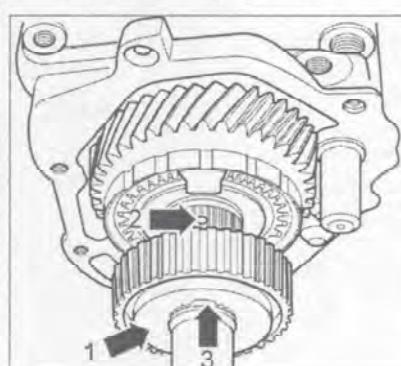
Напрессуйте ступицу синхронизатора 5-й/6-й передач без зазора. Буртик ступицы (стрелка 1) обращен к концу вала. Смазочное отверстие (стрелка 2) вала и паз ступицы синхронизатора (стрелка 3) должны быть совмещены.
